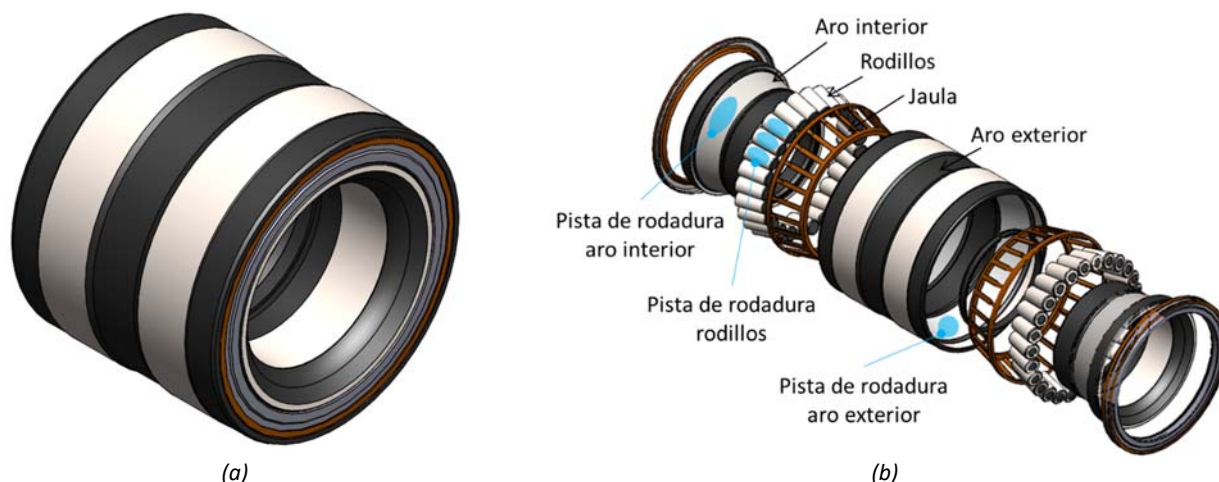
Ejemplo de un rodamiento: (a) conjunto ensamblado, (b) vista explotada de los componentes y pistas de rodadura
